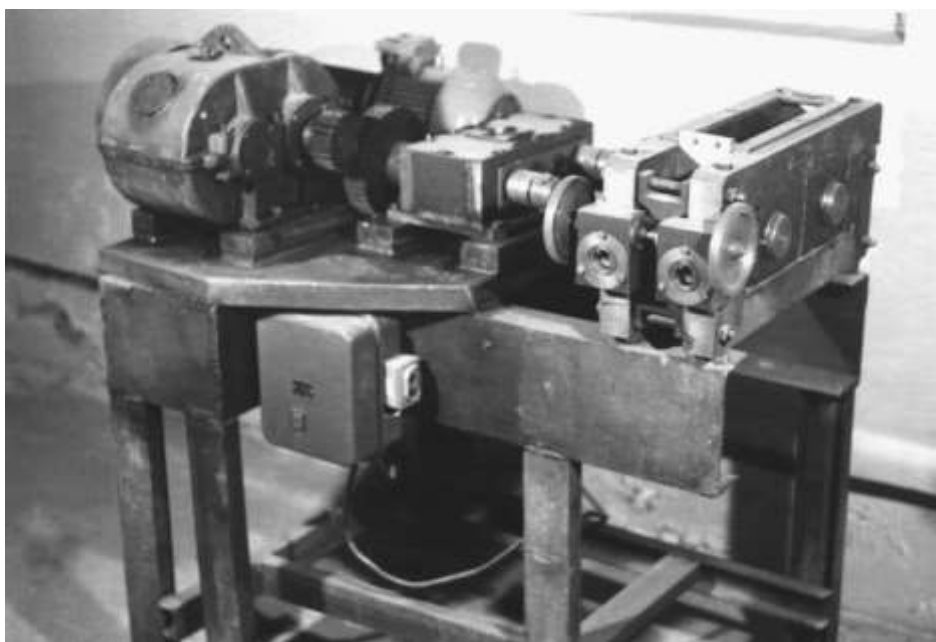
Лабораторний стенд для прокочування композиційних стрічок
